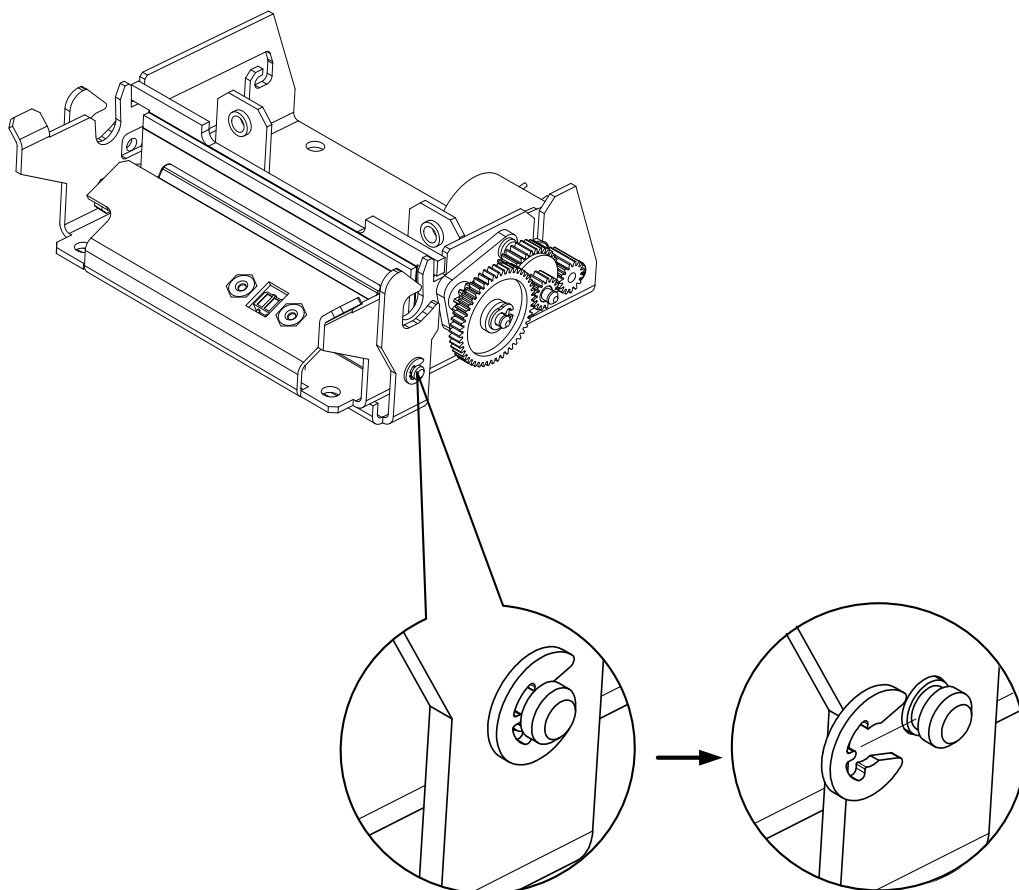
Стопорная шайба оси защелки прижимного вала чековой ленты.
